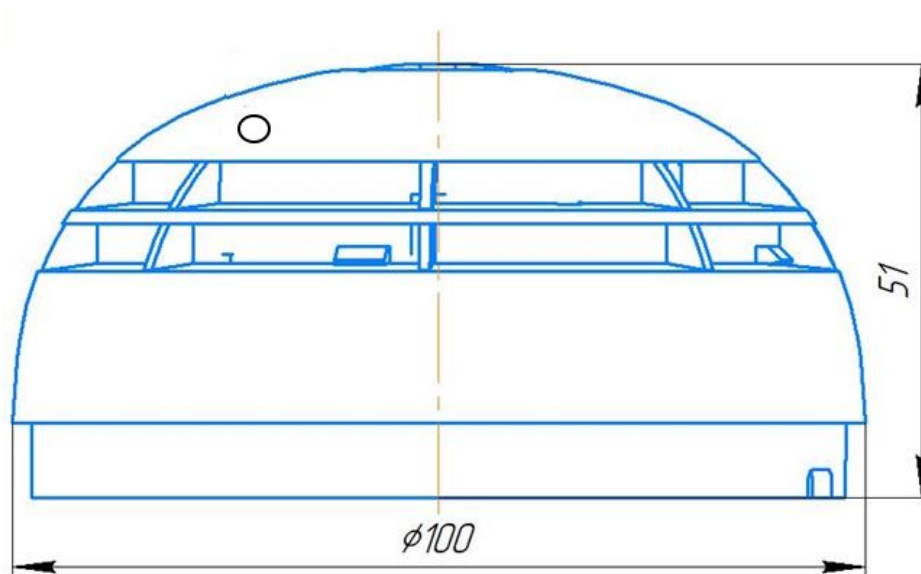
Общий вид звукового пожарного оповещателя с розеткой
